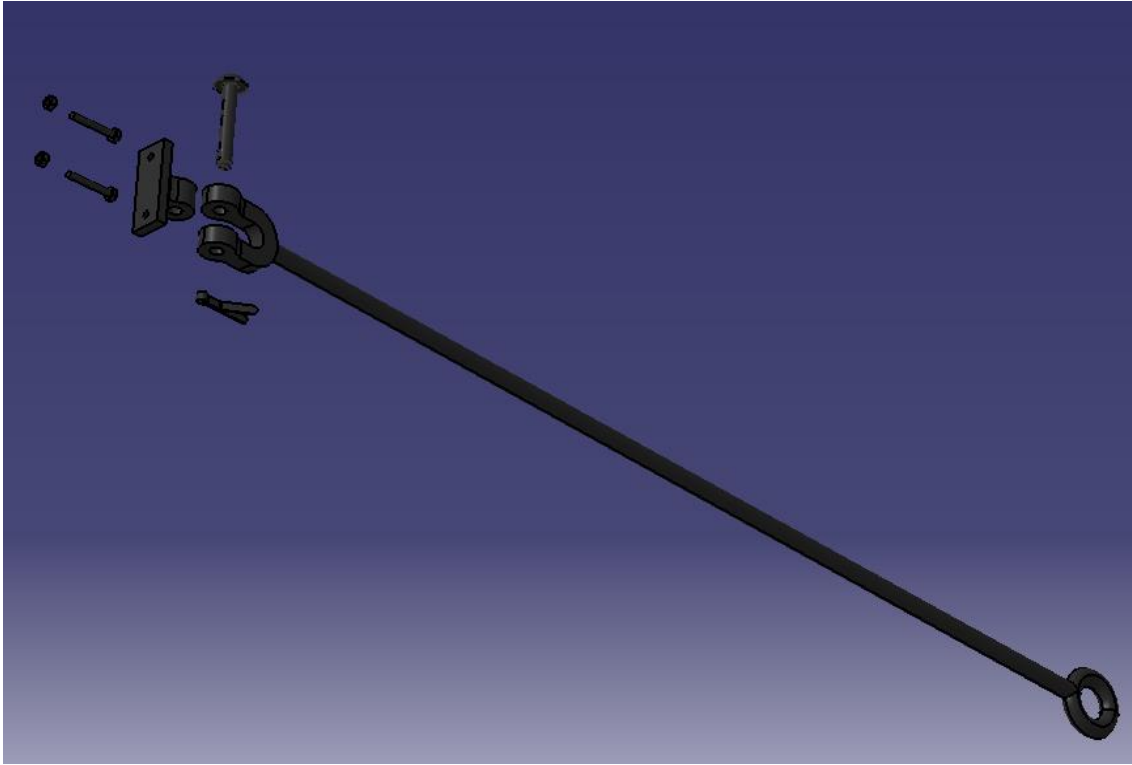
Conjunto enlace delantero-trasero con sus piezas explosionadas
